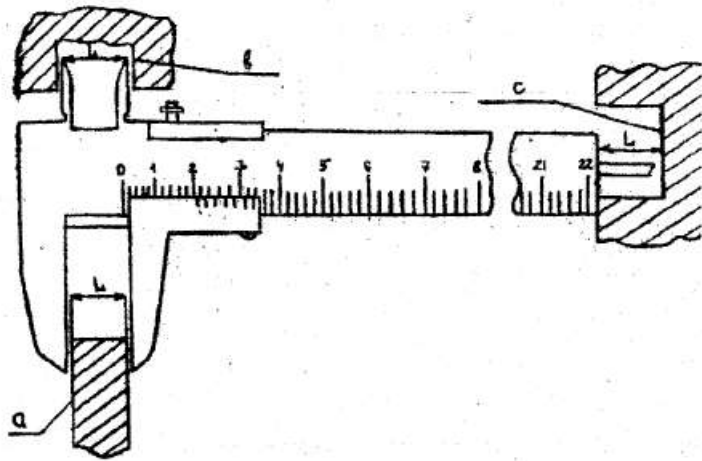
Внешний вид и способы применения штангельциркуля: а) измерение внешнего размера тела; б) измерение диаметра отверстия; с) измерение глубины отверстия.
